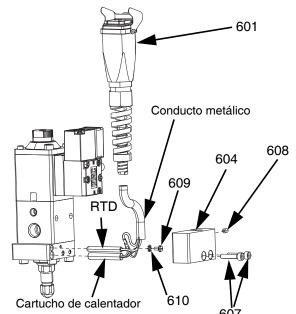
Conjunto de calentador para bloque de salida de 0 mm
